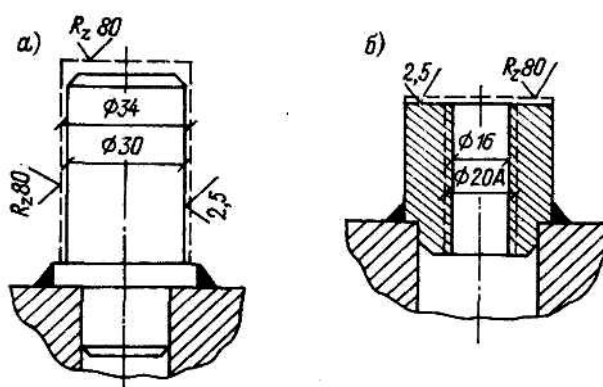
Схема установки фиксаторов с припуском для обработки после сварки: a — пальцев; b — втулок
